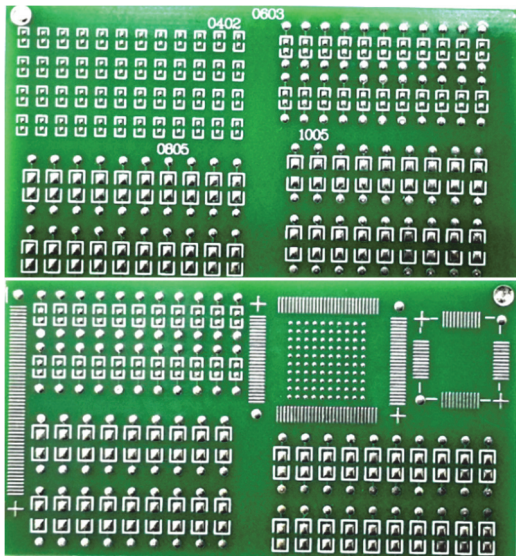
经 OSP 处理的 PCB 板在 3 次回流焊后的上锡效果
